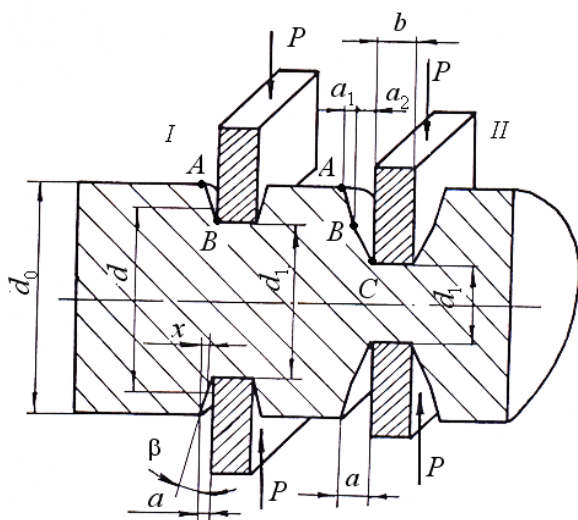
Расчетная схема резки заготовки: I – первый этап резки
